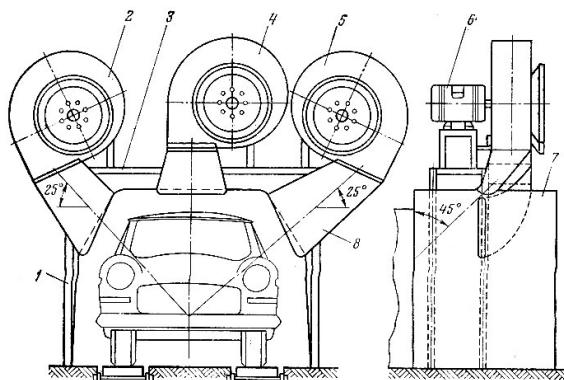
Устройство для сушки (обдува) автомобилей после мойки
